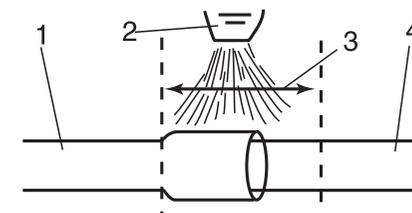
Размещение горелки при пайке труб: 1 — наружная труба; 2 — горелка; 3 — зона нагрева; 4 — внутренняя труба
